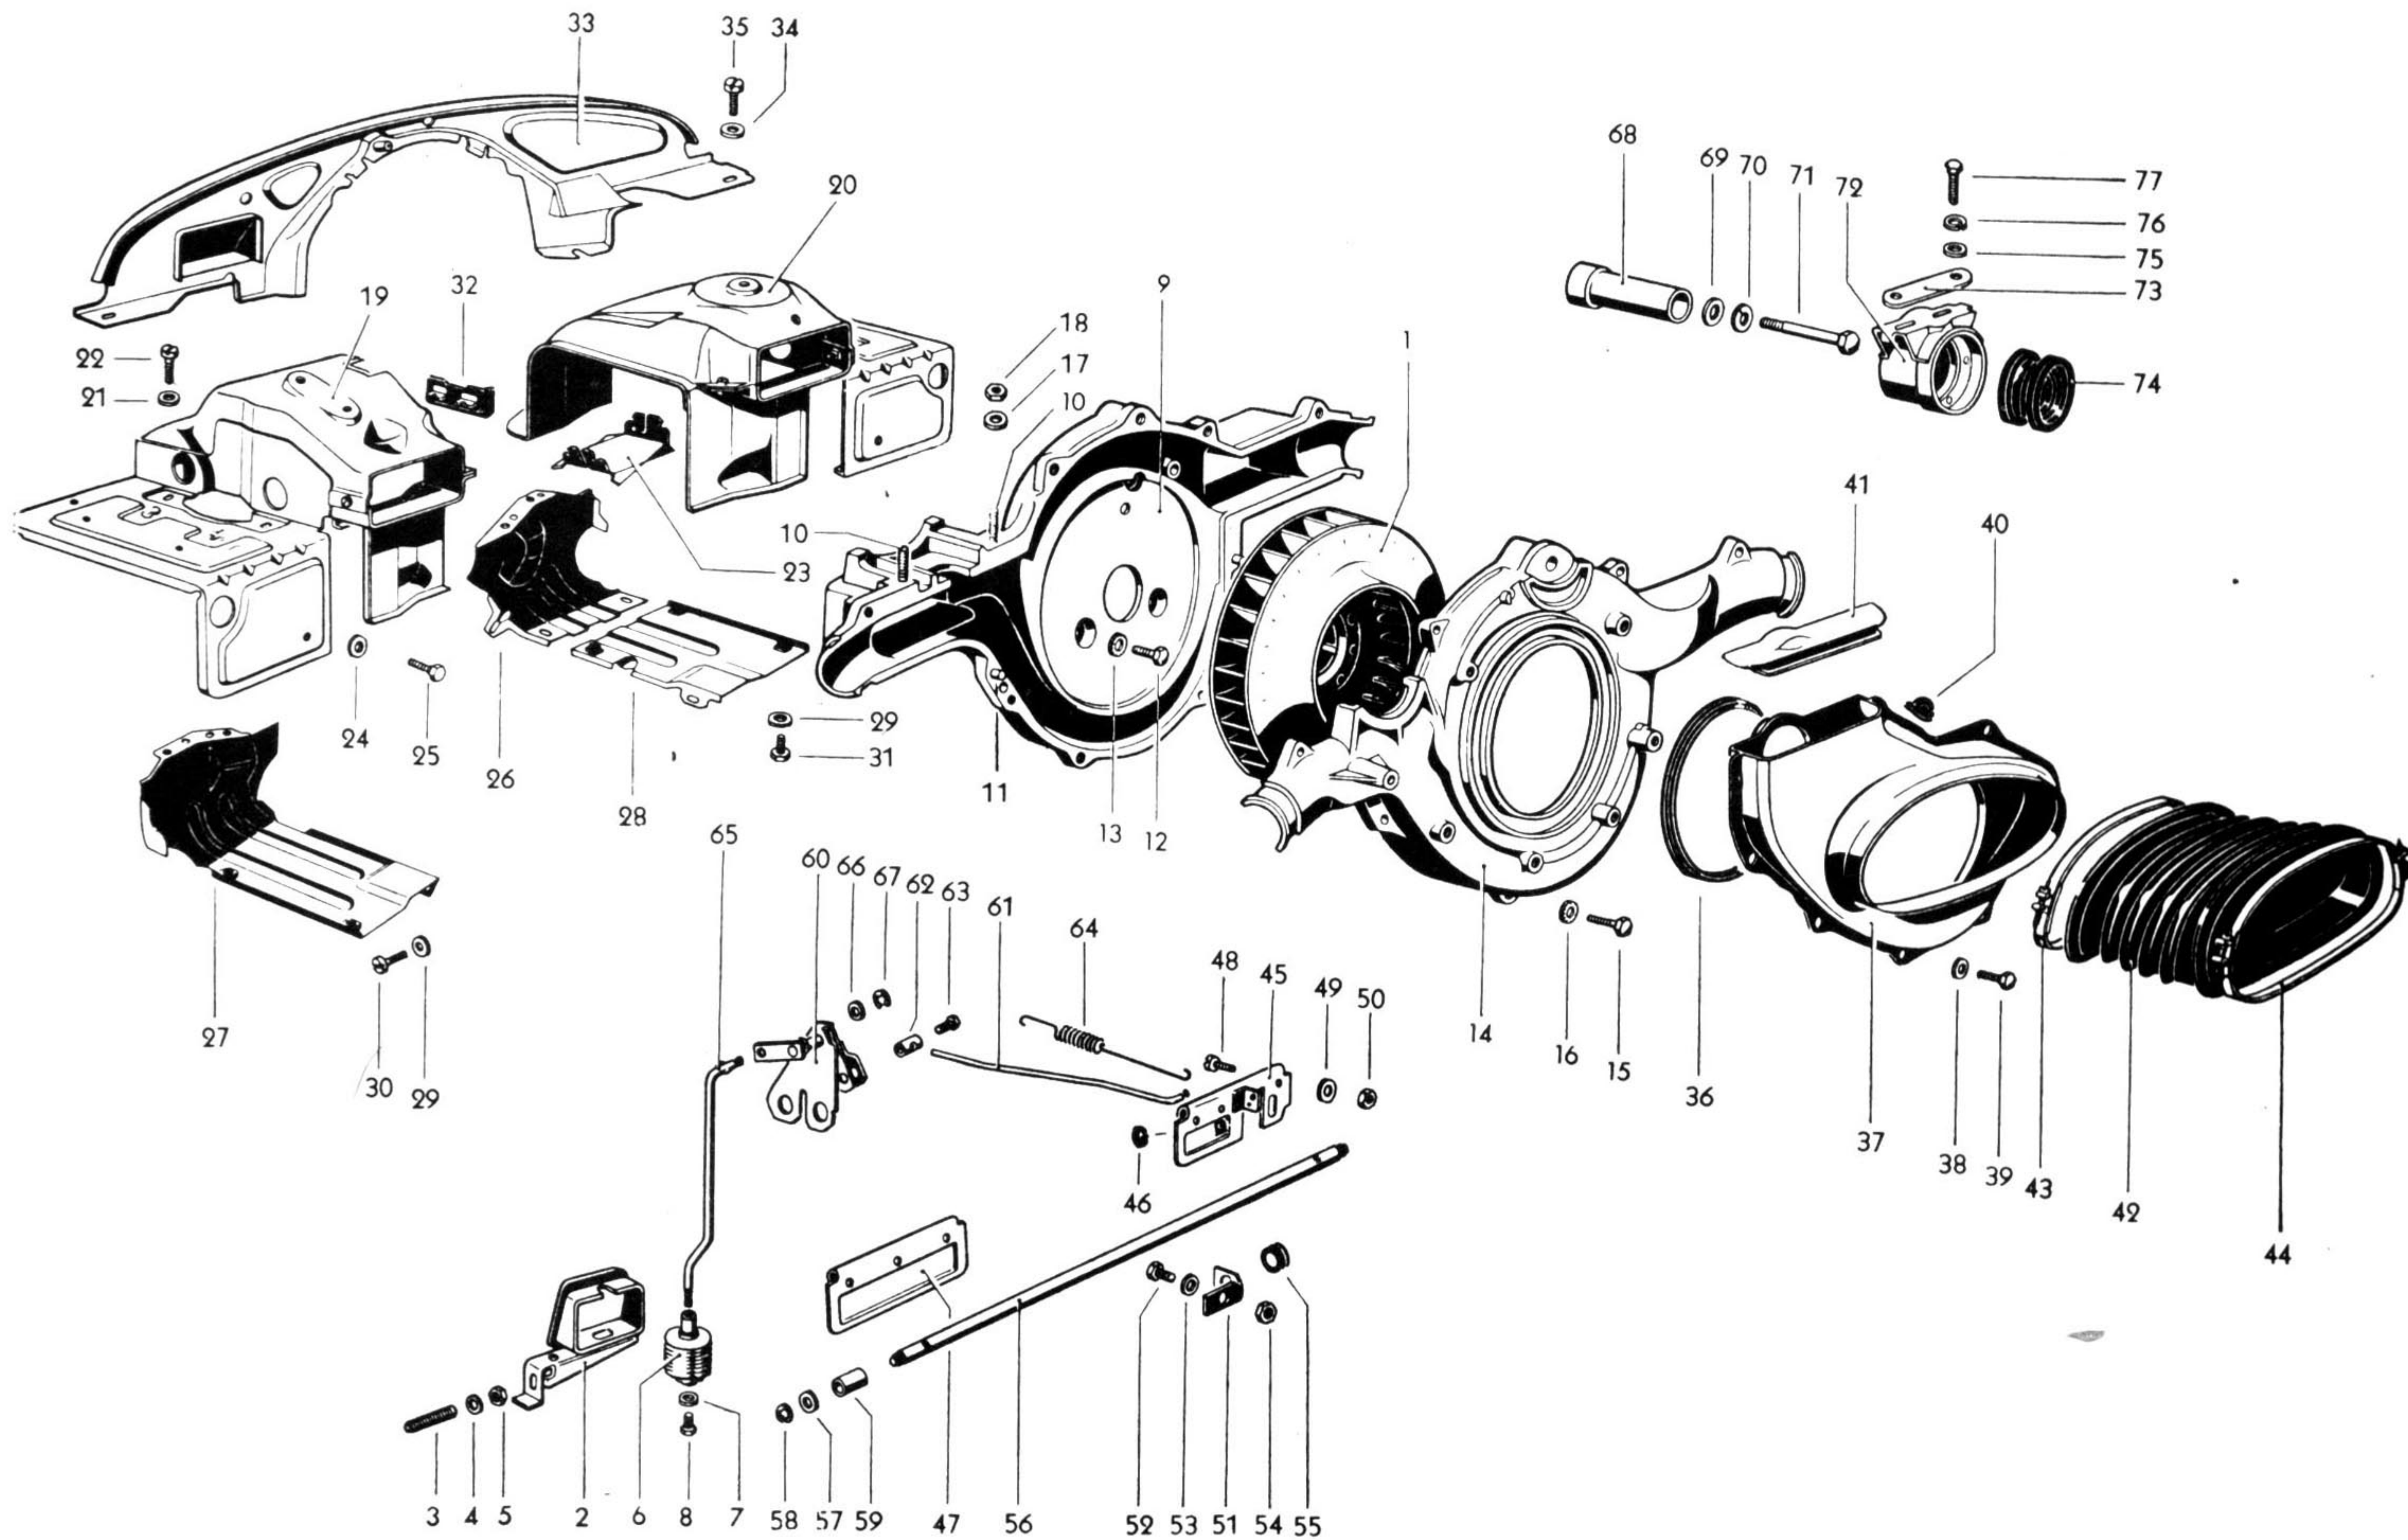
V — Sistema de arrefecimento do motor plano "1 600".
